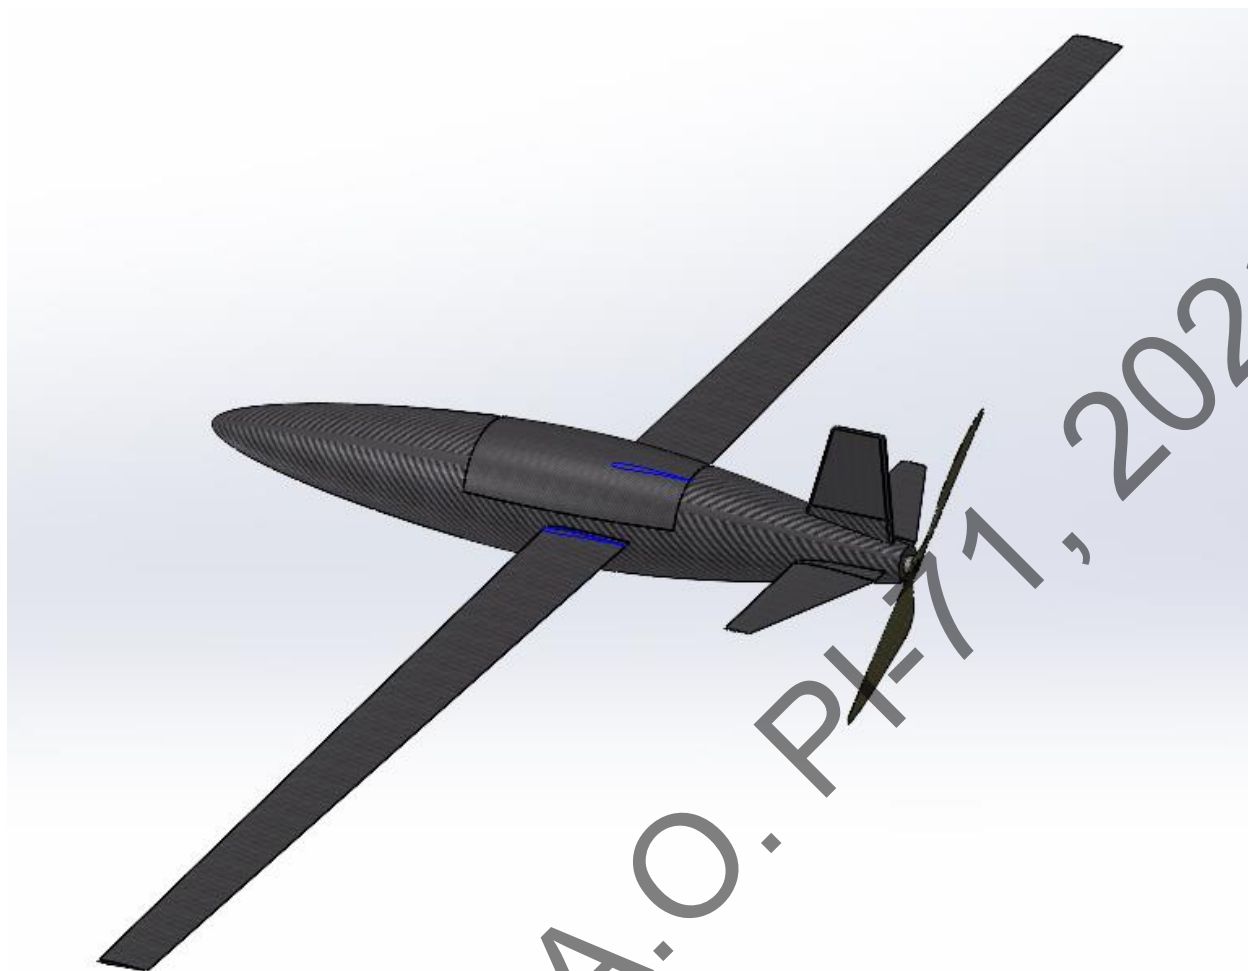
Корпус безпілотної в середовищі SolidWorks
